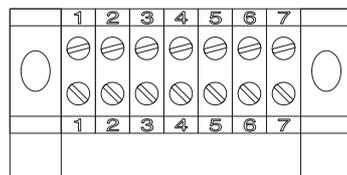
Maßzeichnung DIQ/JB (Maße in mm)
